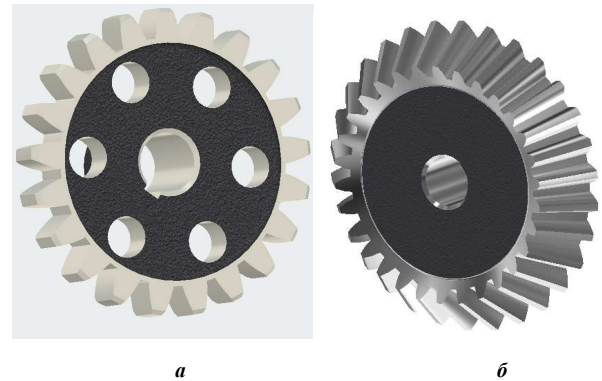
Зубчасте колесо: а – циліндричне; б – конічне
